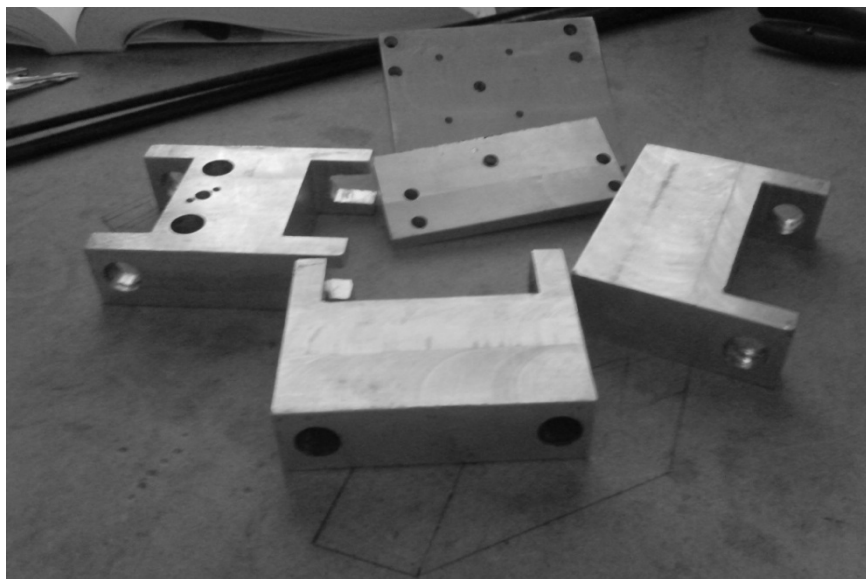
Peças fresadas e furadas prontas para montagem.
